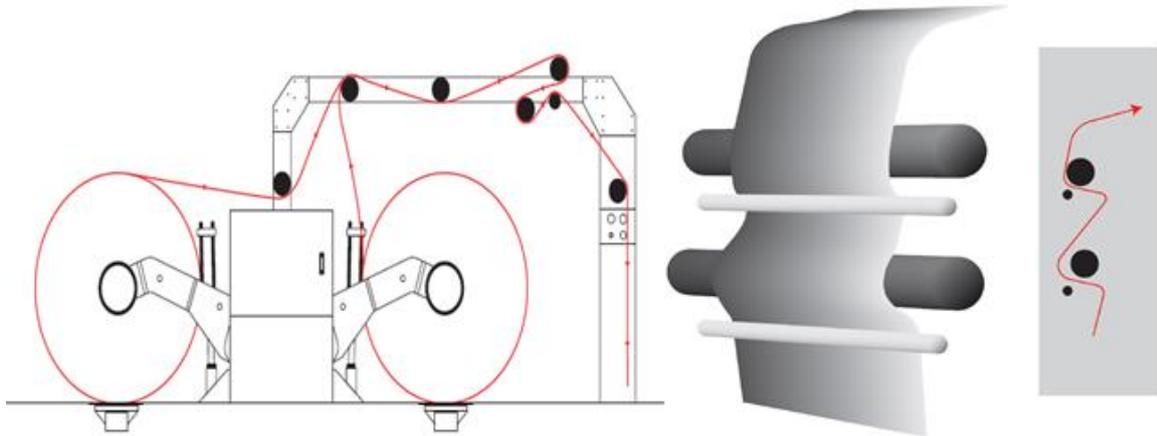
Circuito de Cartolina das bobines com face bobinada para fora
